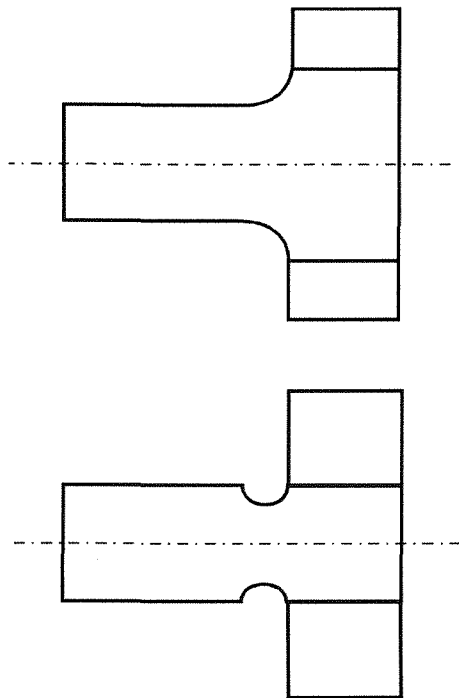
Ejemplos de modificaciones de diseño para reducir tensiones en uniones eje-cubo.
